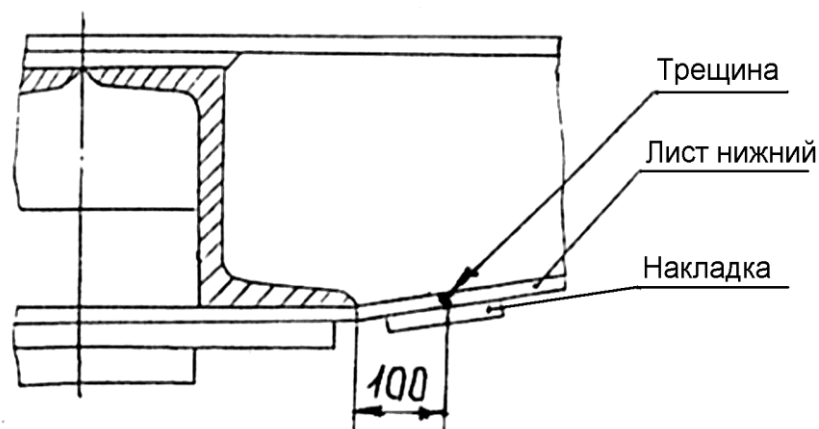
Нижний лист шкворневой балки, отремонтированный сваркой
